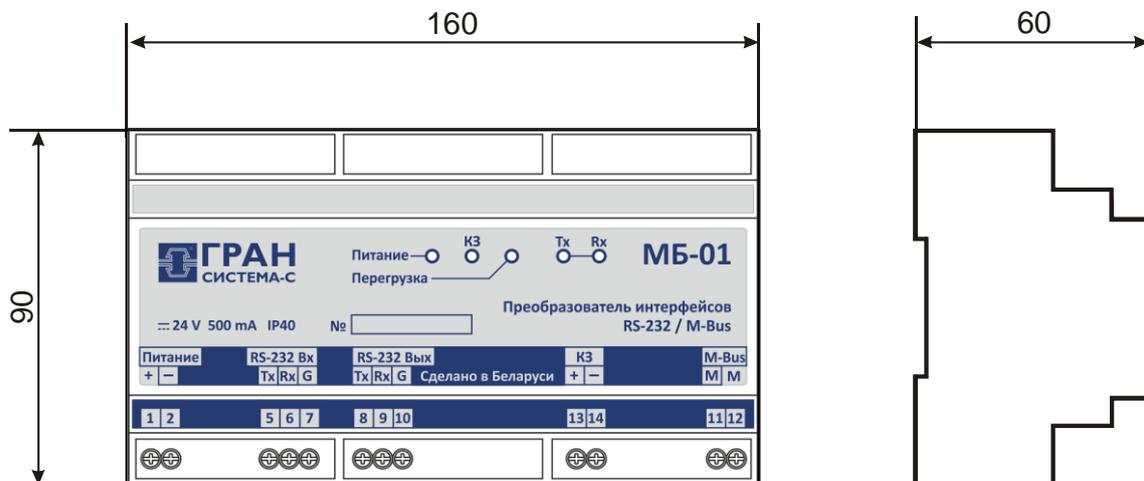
Габаритные размеры преобразователя МБ-01
